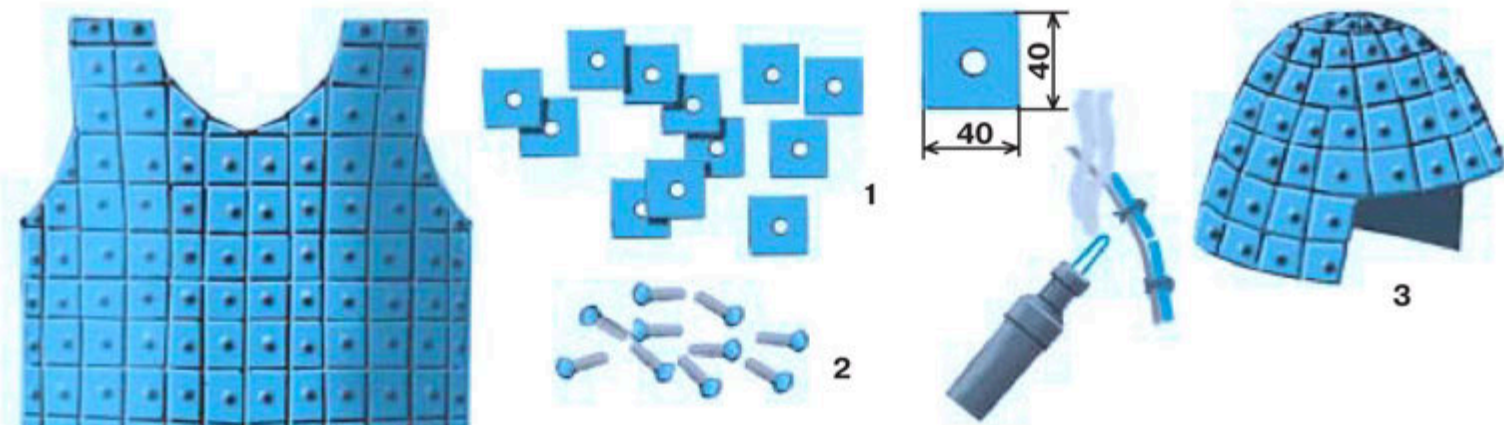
Изготовление шлема воина с тяжелым вооружением: 1 — размеры и общий вид полистироловых пластинок; 2 — пластиковые заклепки; 3 — общий вид шлема.
